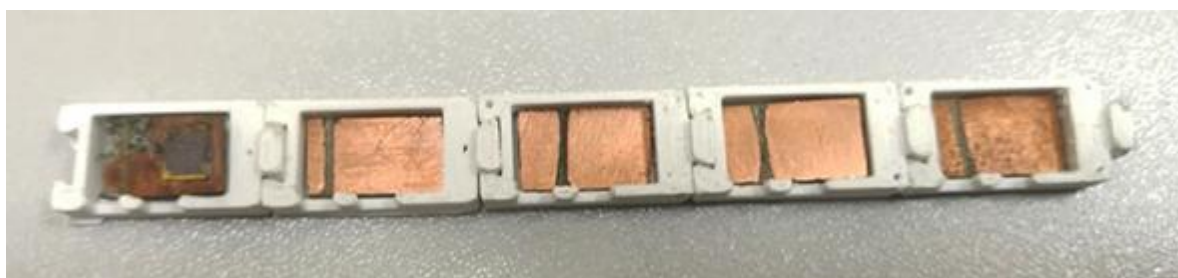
Сборка из 5-и корпусов с фотоэлементами. Крышки корпусов сняты.
